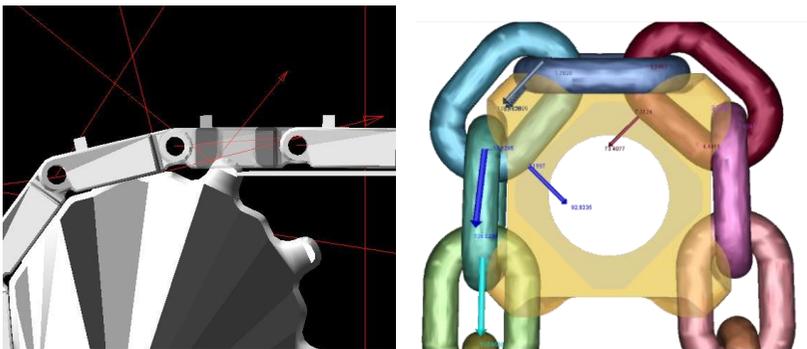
Raupenkettenfahrwerk (Gelenkkette) und Rundstahlkettentrieb (Details) in MKS
